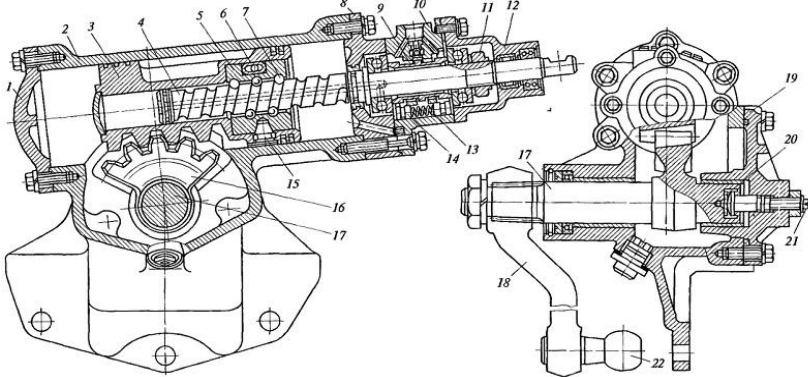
Рульовий механізм типу “гвинт-гайка-рейка-сектор” (1-кришка циліндру; 2- картер рульового механізму; 3-поршень-рейка; 4-гвинт; 5-кулькова гайка; ; 6-кулькова канавка; 7-кульки; 8-проміжкова кришка; 9-золотник; 10-корпус клапану керування; 11-гайка; 12-верхня кришка; 13-пружина плунжеру; 14-плунжер; 15-стопорний гвинт; 16-зубчастий сектор; 17-вал; 18-сошка; 19-бокова кришка; 20-стопорне кільце; 21-гвинт регулювання; 22-кульовий палець).
